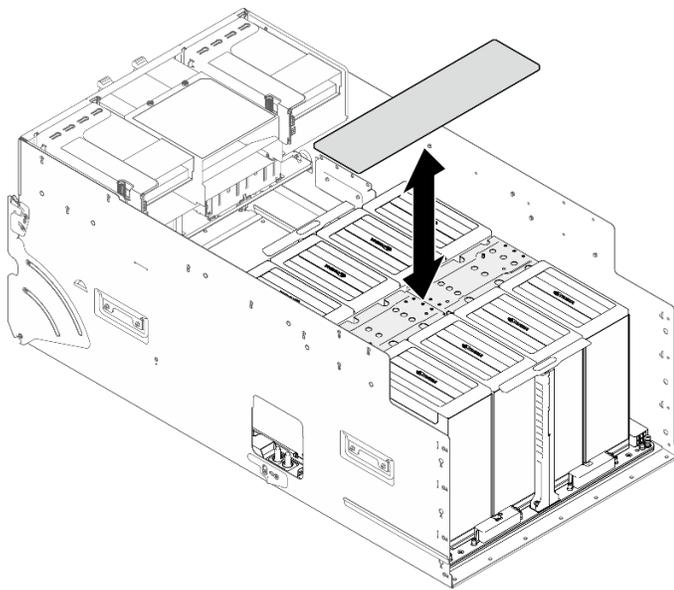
Remoção da tampa do dissipador de calor NVSwitch
